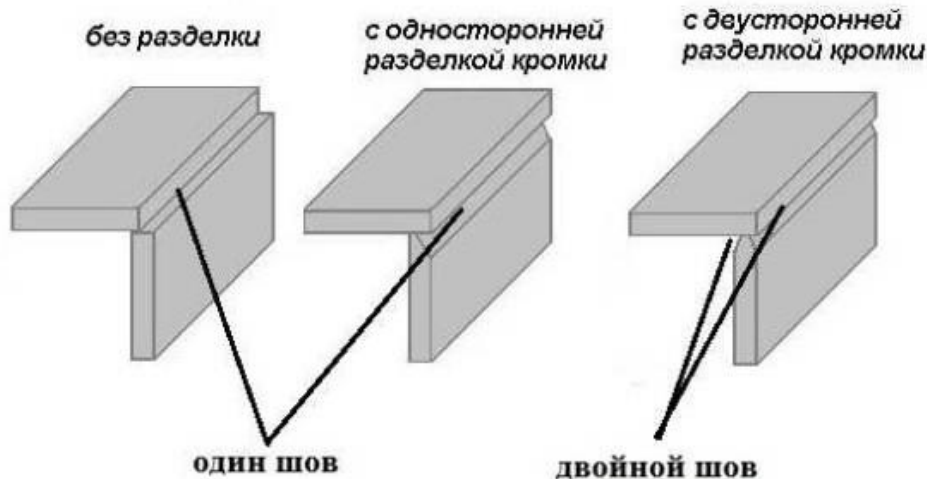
Как подготавливать металл для углового соединения (с одним или двумя швами)
